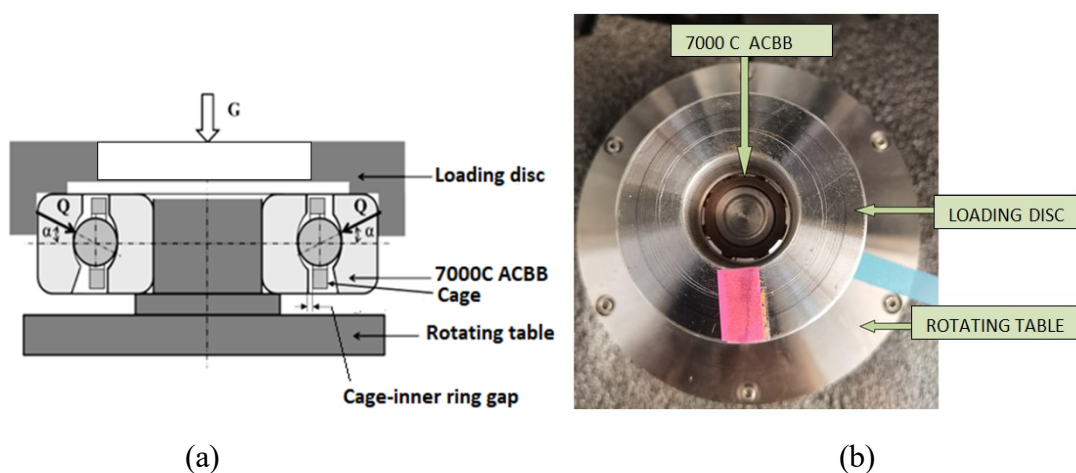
(a) Schema de montare a rulmentului 7000C; (b) Vederea superioară a carcasei și a mesei rotative în mișcare cu indicatorii specifici pentru turație
